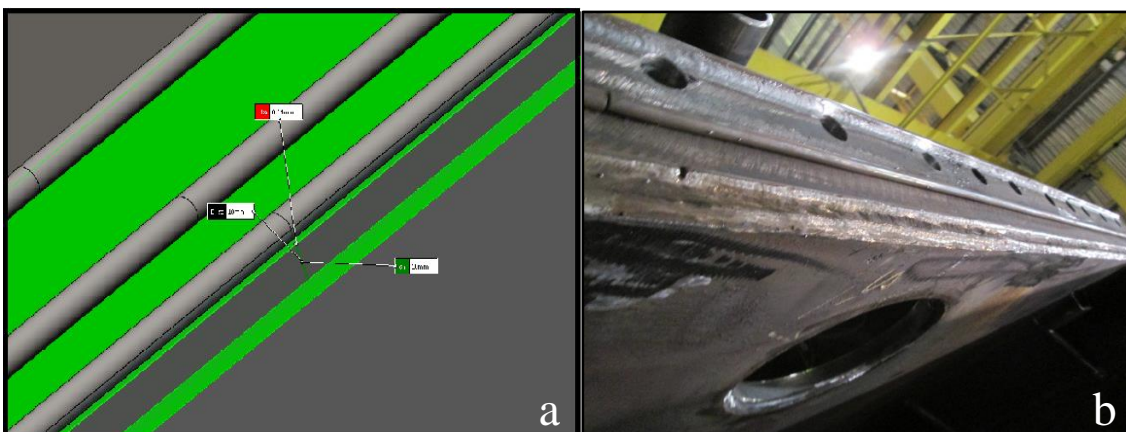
Desenho de montagem flange fechamento e 6b Solda do cinto
